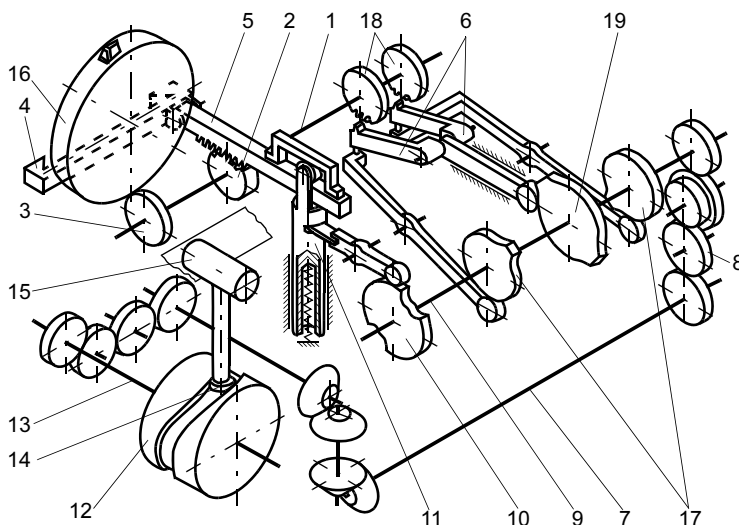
Кинематическая схема обкатно-делительного приспособления
